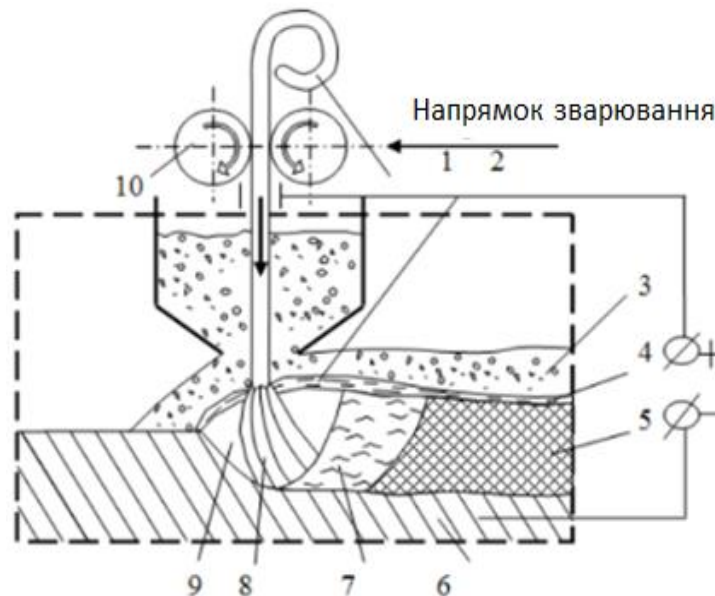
Схема процесу автоматичного зварювання під шаром флюсу: 1– електрод; 2 – рідкий флюс; 3 – сипучий флюс; 4 – спік флюсу; 5 – закристалізований метал шва; 6 – метал, що зварюється; 7 – розплавлений метал шва; 8 – зона електричної дуги; 9 – газовий міхур; 10 – ролики
